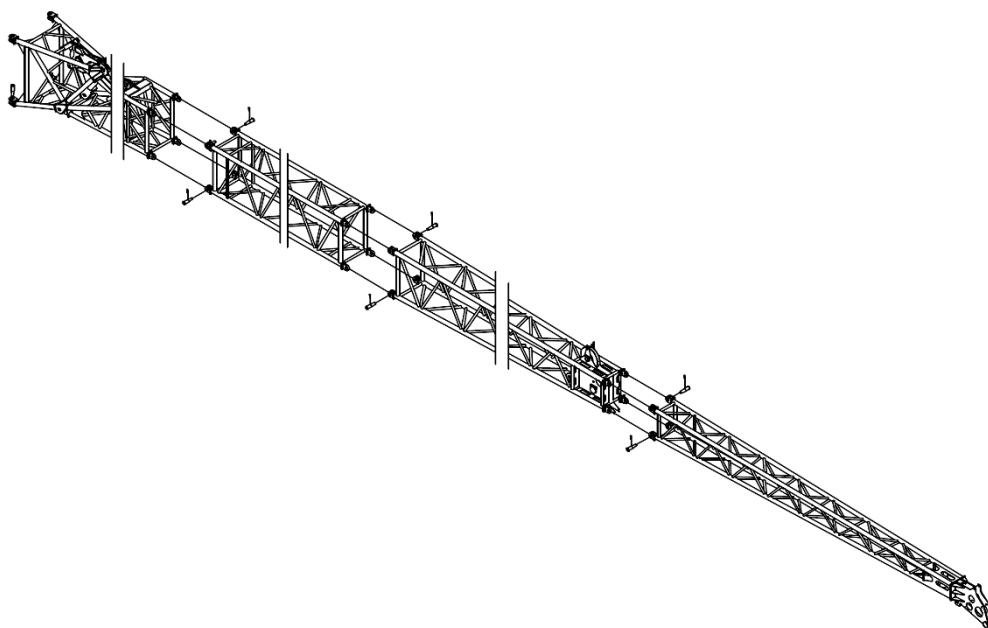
Conexão da lança principal e variante de braço 3 (28 m)
